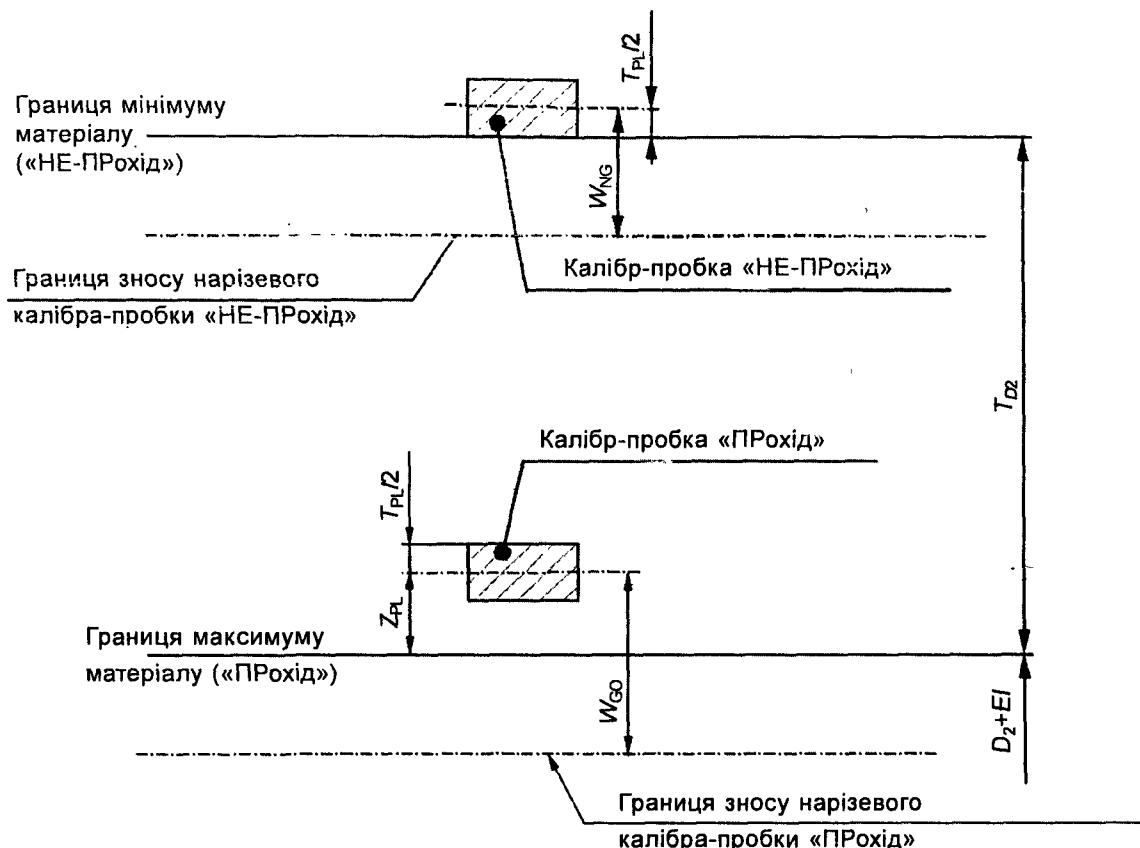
Поля допусків середнього діаметра гладких калібрів для контролювання внутрішніх нарізей (схема розташування)
